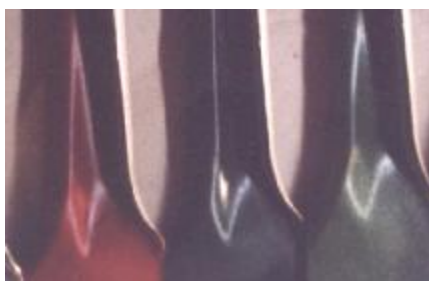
Неустойчивость захвата входного участка заготовки
